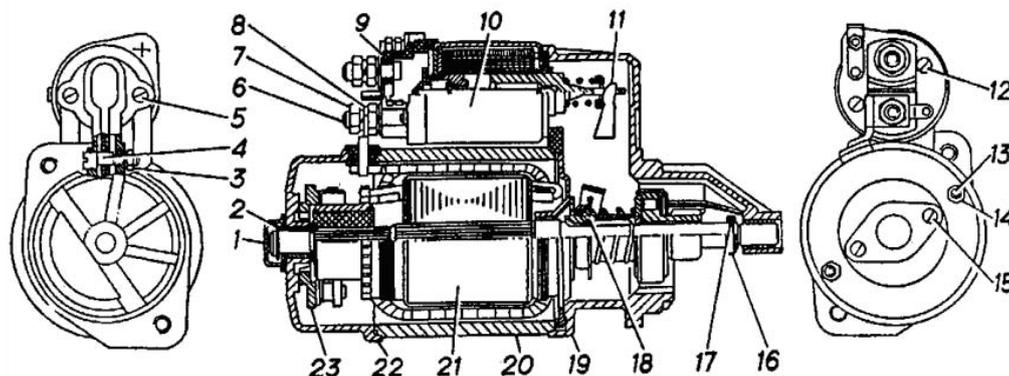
Стартер. 1 - колпак; 2 - стопорная шайба; 3 - гайка; 4 - ось рычага; 5 - винты; 6 - вывод дной болт; 7 - гайка; 8 - вывод; 9 - крышка реле; 10 - тяговое реле; 11 - рычаг; 12 - винты; 13 - стяжная шпилька; 14 - гайка; 15 - винты; 16 - упорное кольцо; 17 - замковое кольцо; 18 - привод; 19 - крышка со стороны привода; 20 - корпус; 21 - якорь; 22 - крышка со стороны коллектора; 23 - траверса.
